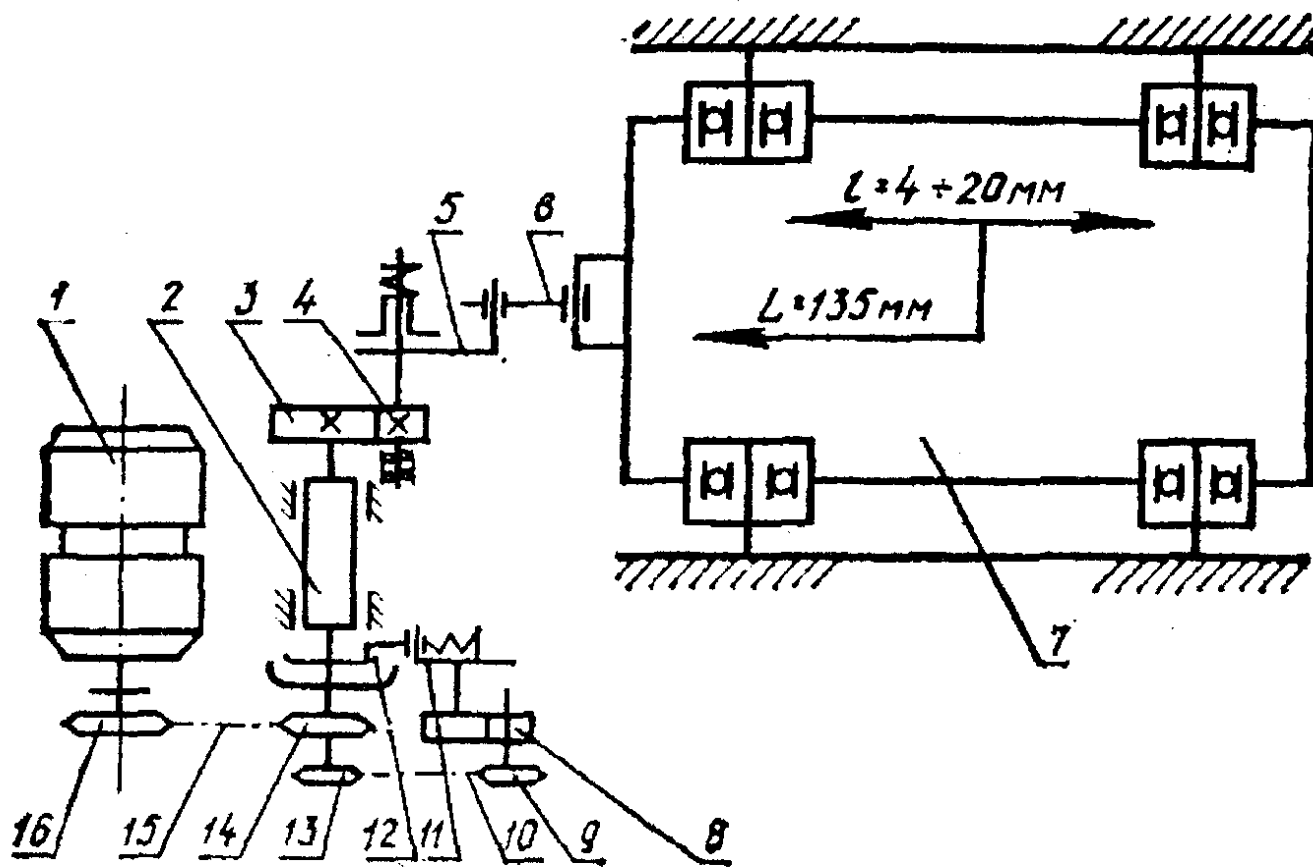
Схема привода каретки сушилки СЗШ-16:
